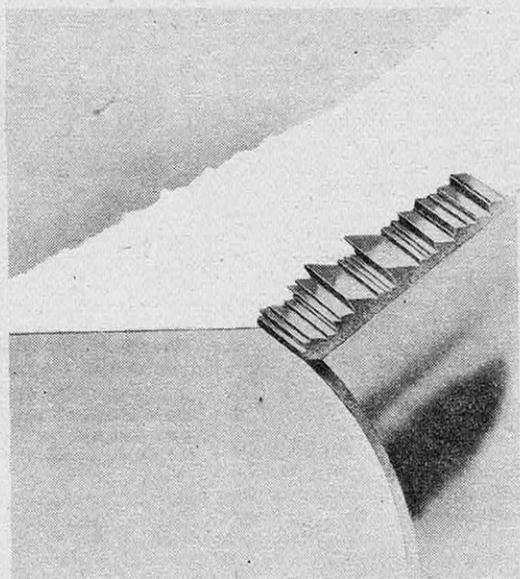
LE TRAITEMENT DES ÉPROUVETTES CYLINDRIQUES POUR EXAMEN MICROGRAPHIQUE DES SURFACES
